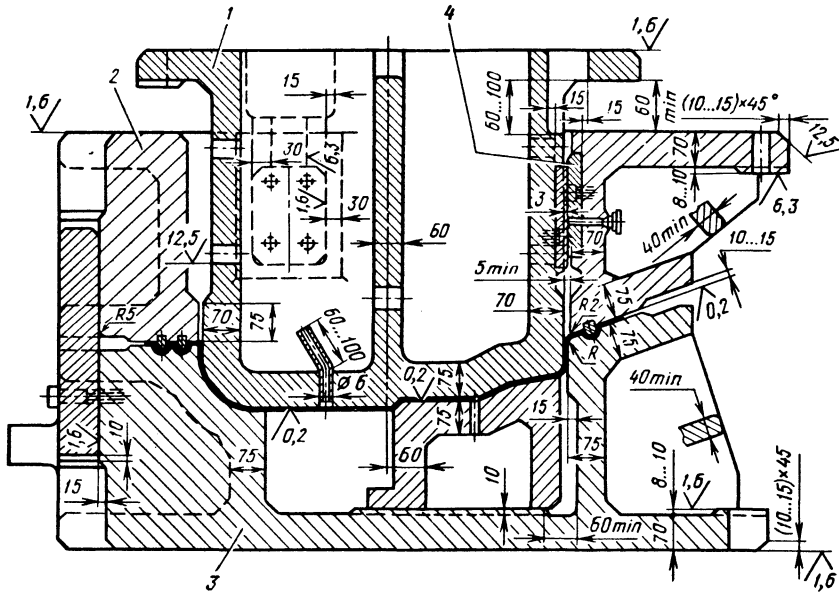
Штамп для вытяжки крупногабаритной детали на прессе двойного действия
